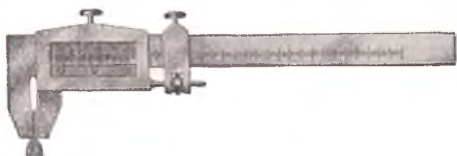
Штангенциркуль с микрометрическим винтом и двумя губками
